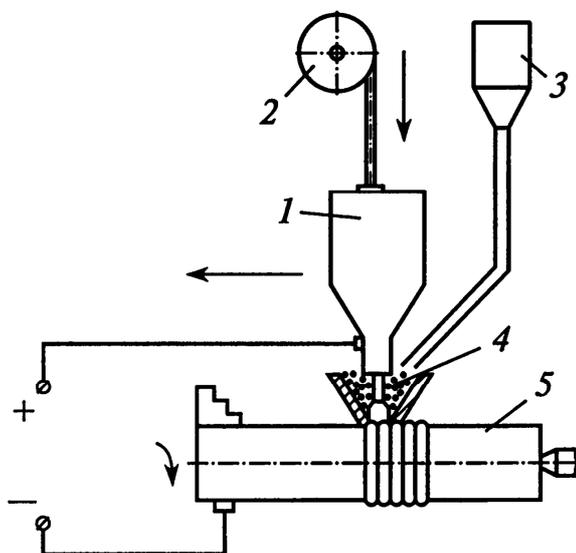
Схема автоматической дуговой наплавки под флюсом:
